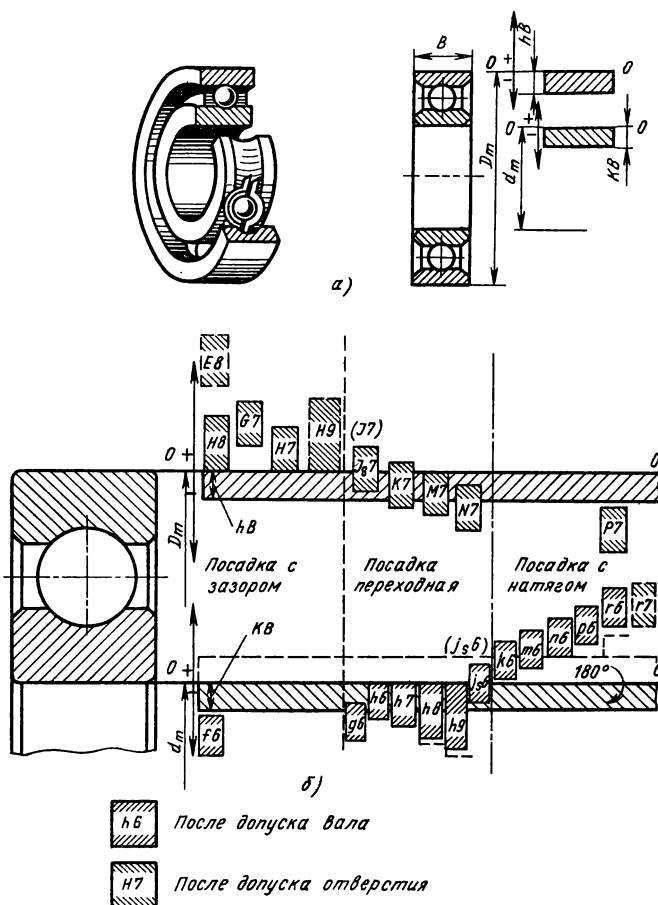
Поля допусков подшипника качения по наружному D и внутреннему d диаметрам (а); схема расположения полей допусков валов и отверстий (б), сопрягаемых с подшипниками качения 0-го и 6-го классов точности
